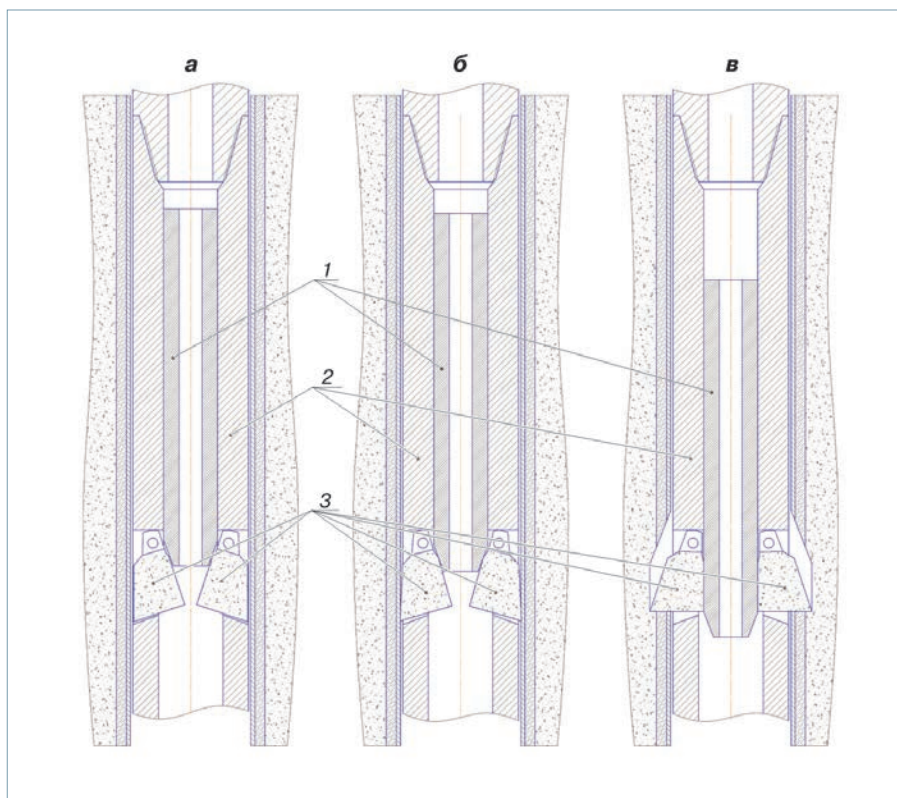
Принципиальная схема активации раздвижного фрезера: а – транспортное положение; б – врезка в обсадную колонну; в – рабочее положение; 1 – толкатель; 2 – корпус фрезера; 3 – лопасти
